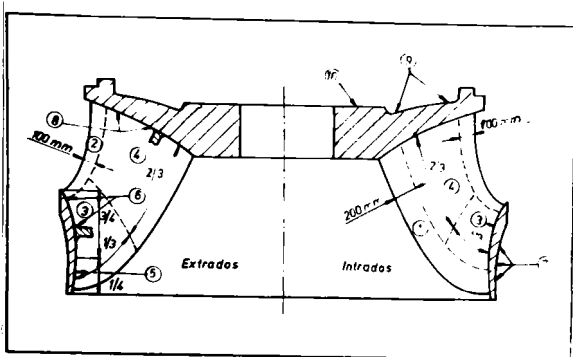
Zone de inspecție pentru rotoare Francis.
